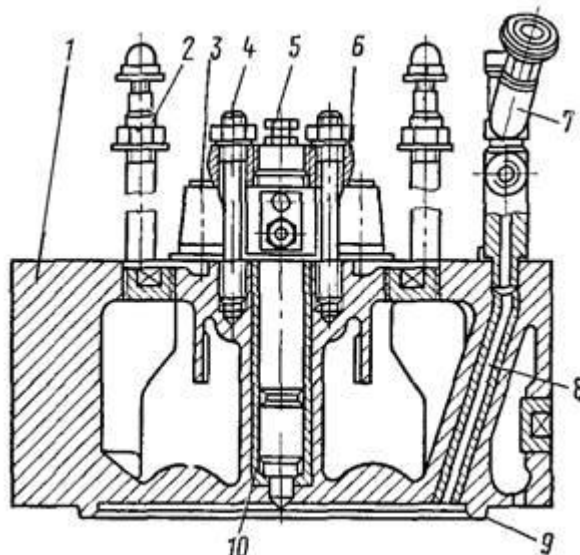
Крышка цилиндра: 1 - корпус, 2, 4 - шпильки; 3 - направляющие втулки впускного и выпускного клапанов, 5 - форсунка, 6 - фланец, 7 - кран индикаторный, 8 - трубка, 9 - бурт уплотнительный, 10 – гильза.
